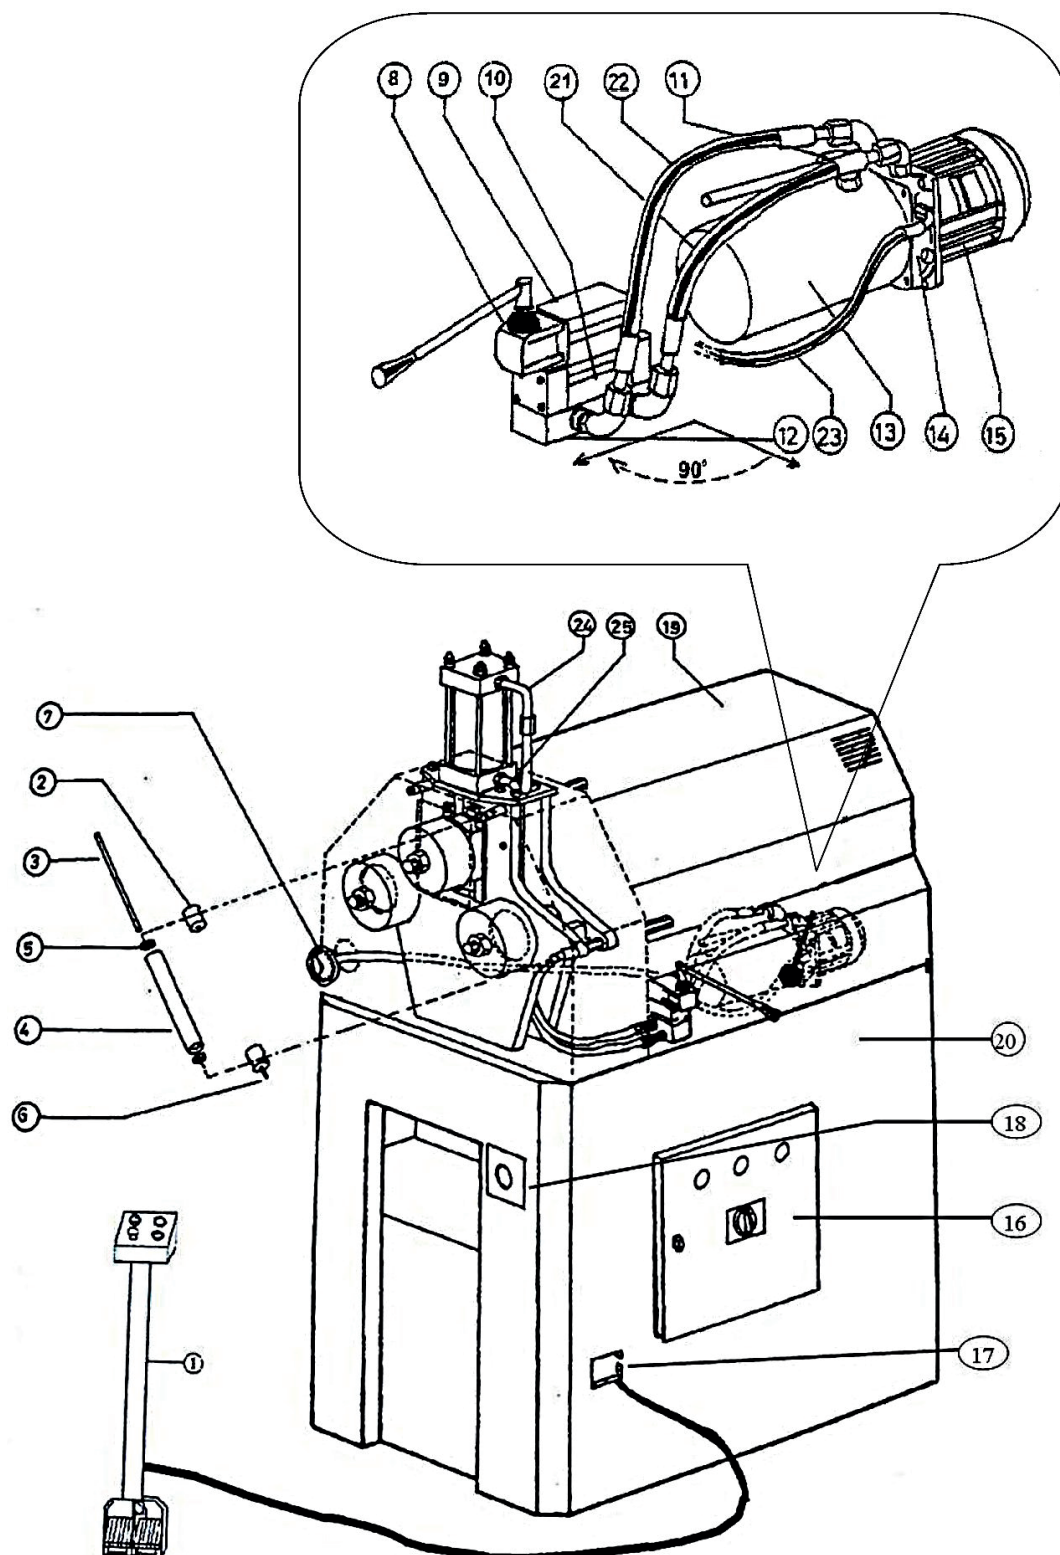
Dessin des pièces détachées 1 - Châssis PRM 50 FH
